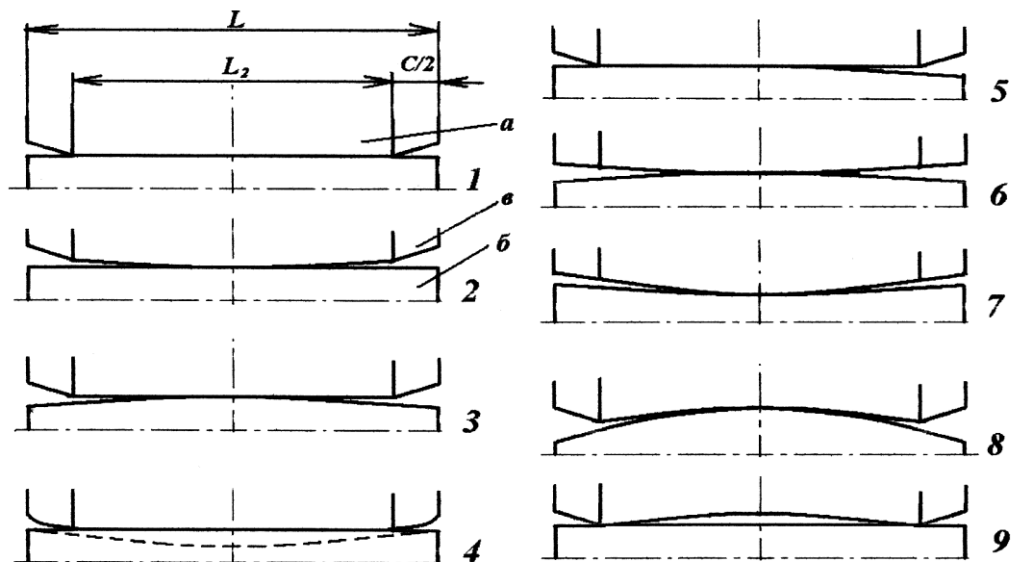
Типи профілів твірних валків: а - опорний валок; б- робочий валок; 3- кінцевий скіс
